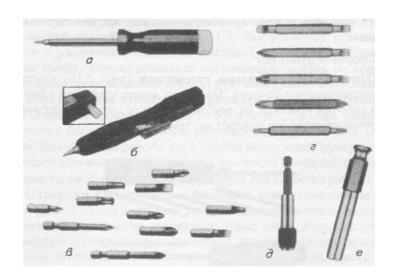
Отвертки со сменными насадками и принадлежности к ним: a — отвертка с магазином для насадок под крышкой ручки; δ — отвертка с «ящичком» в ручке; ϵ — отверточные насадки с одним рабочим профилем; ϵ — насадки с двумя рабочими профилями;
